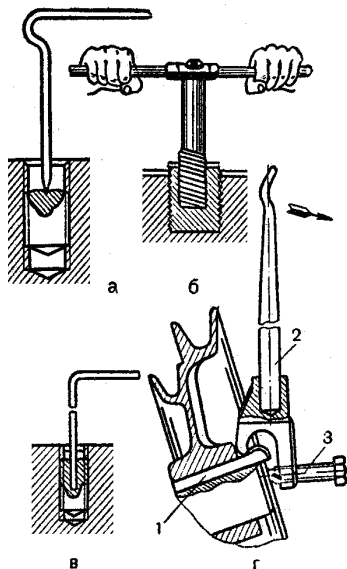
Удаление сломанных шпилек и болтов: а – вывертывание сломанной шпильки отверткой; б – вывертывание сломанной шпильки болтом; в – вывертывание сломанной шпильки четырехгранником; г – удаление шпонки приспособлением; 1 – шпонка; 2 – рычаг; 3 – винт
